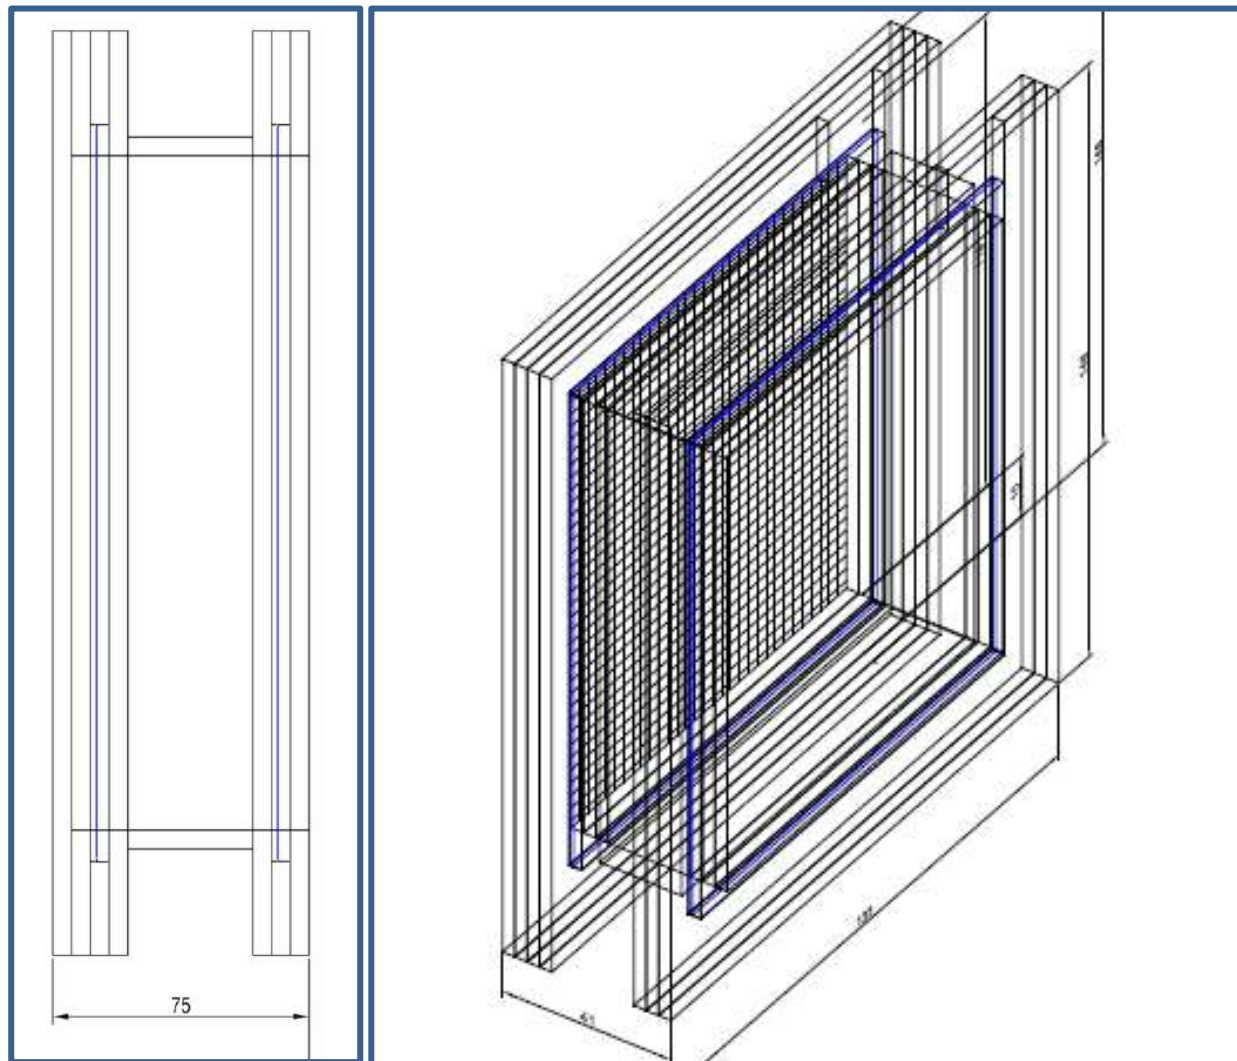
Vista frontal del diseño de cuba de una CCM, dimensiones en mm.
